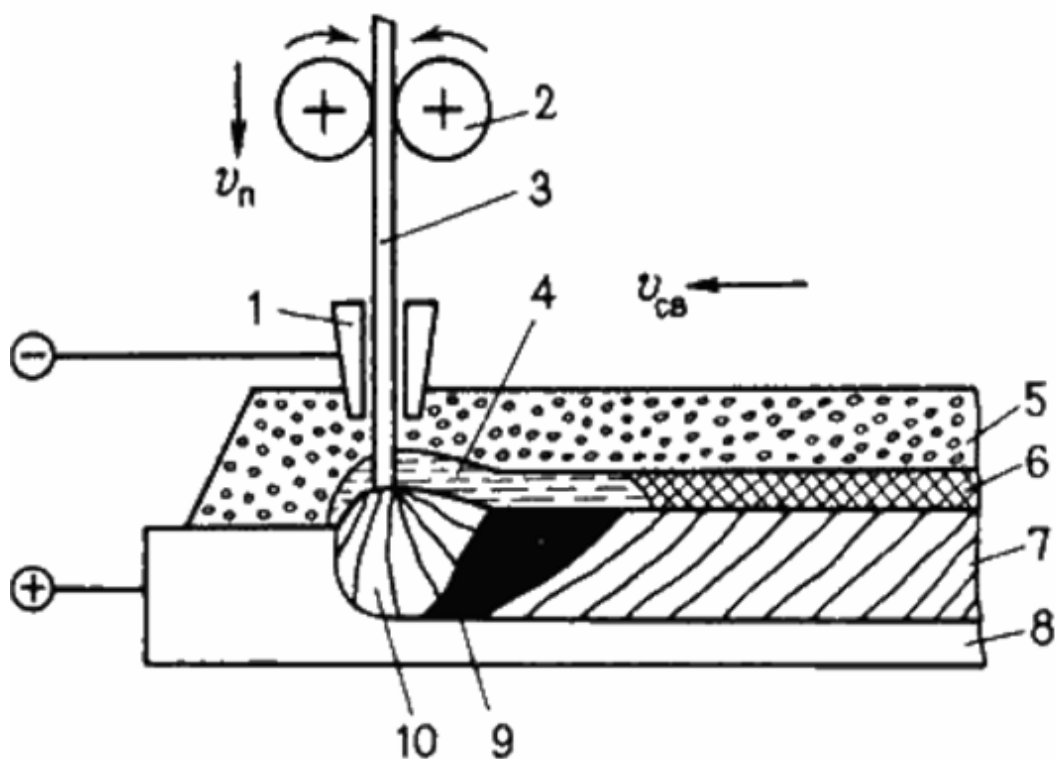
Схема механизированной наплавки металла под слоем флюса: 1 – токоподводящие колодки; 2 – подающие ролики; 3 – электродная проволока; 4 – слой шлака; 5 – слой сухого флюса; 6 – шлаковая корка; 7 – сварной шов (наплавленный металл); 8 – основной металл; 9 – сварочная ванна; 10 – электрическая дуга
